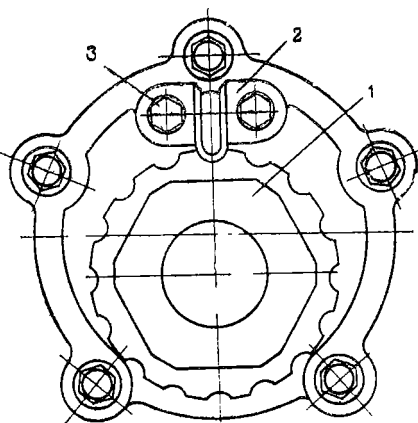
Крепление стопора гайки боковой крышки рулевого механизма:
